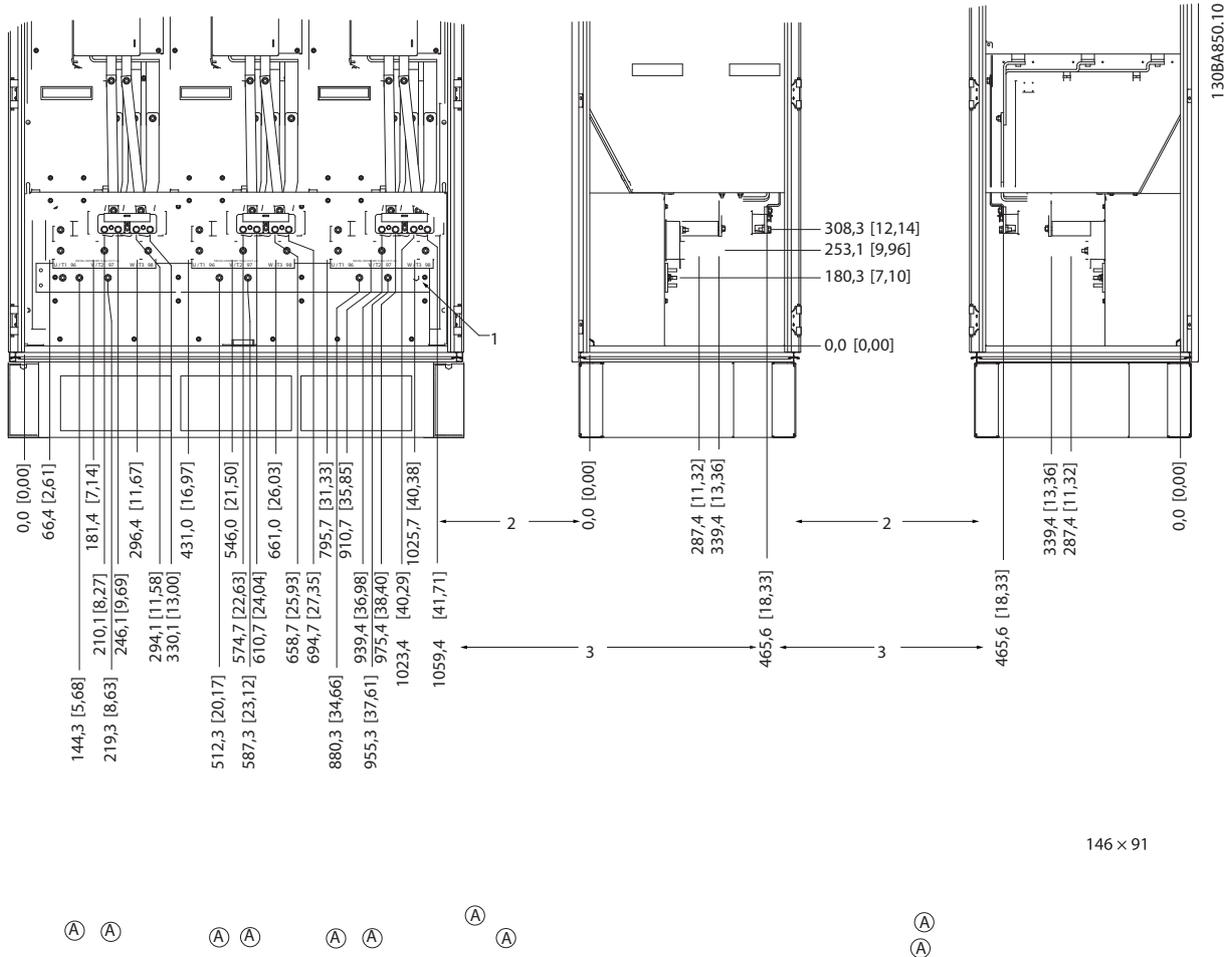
Ubicación de los terminales - Armario del inversor - F2 y F4 (vista frontal y lateral derecho e izquierdo). La placa prensacables está 42 mm por debajo del nivel 0.
